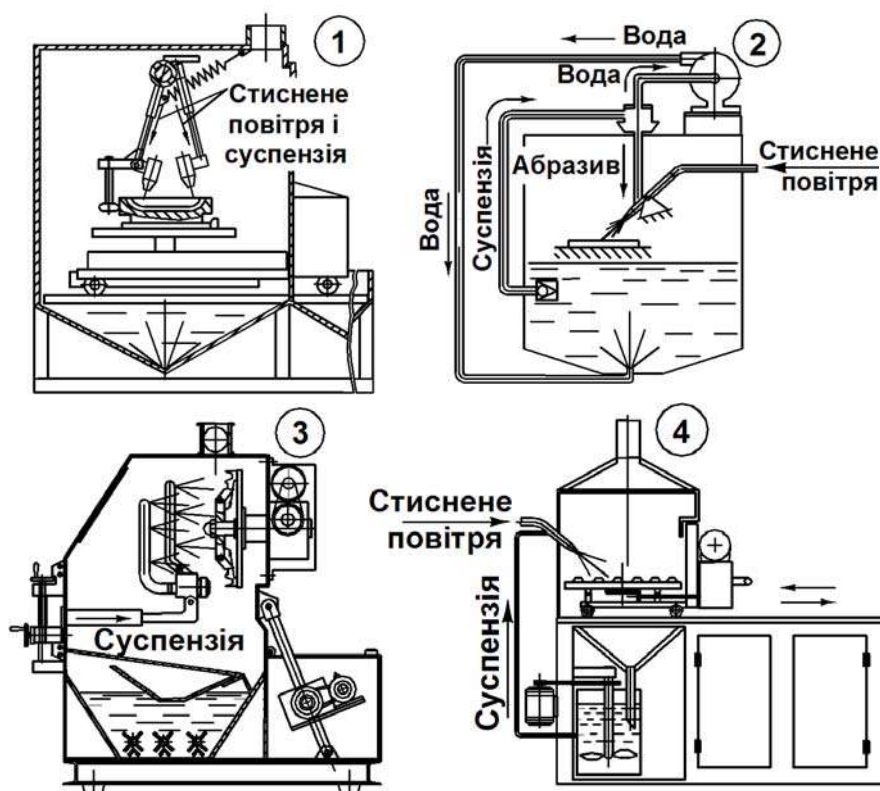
Принципові схеми струминних установок для обробки абразивною суспензією, що перемішується барботуванням
